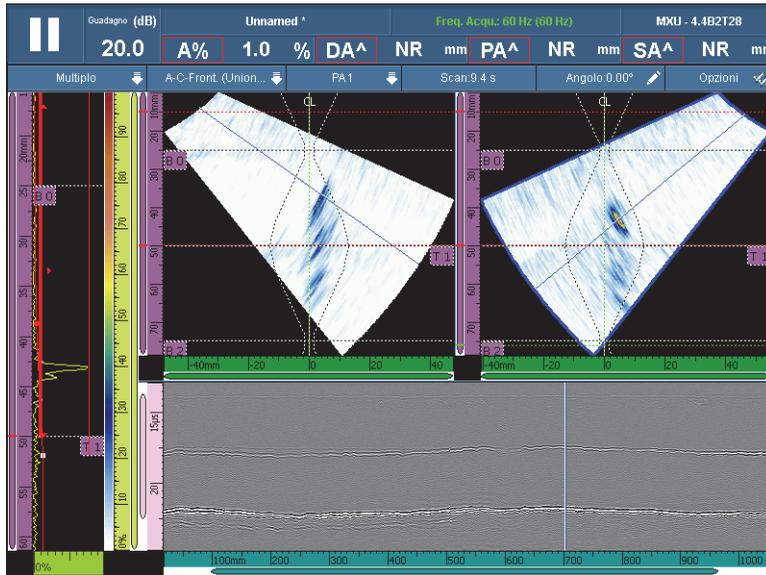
Un esempio di layout PA-UT Weld (A-B-S)
